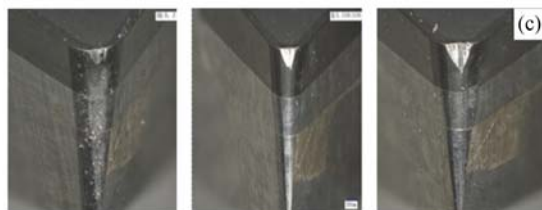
所示为切削路程分别为283.4 m、368.3 m和584.4 m时不同切削条件下的刀具磨损形貌图。可以看出,4种切削方式下刀具后刀面均形成三角形状的磨损带。在切削距离为283.4 m时刀具出现了较程度的磨损,后刀面磨损带内出现了沿切削方向的沟槽,且常规切削和激光加热辅助切削时的磨损程度最为严重,其次是超声振动切削,激光超声复合切削时刀具后刀面磨损较轻。此时4种切削方式下刀具均处于初期磨损状态。
